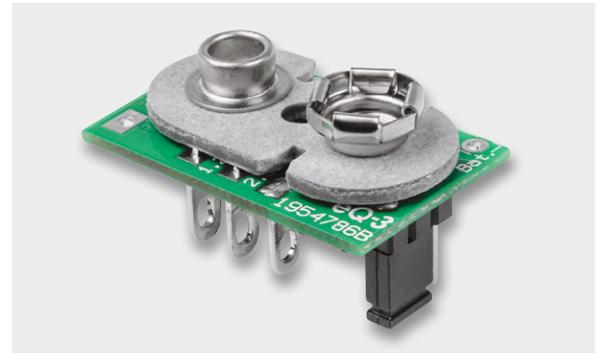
Platine mit eingelöteter Druckknopf-Kontaktplatte
